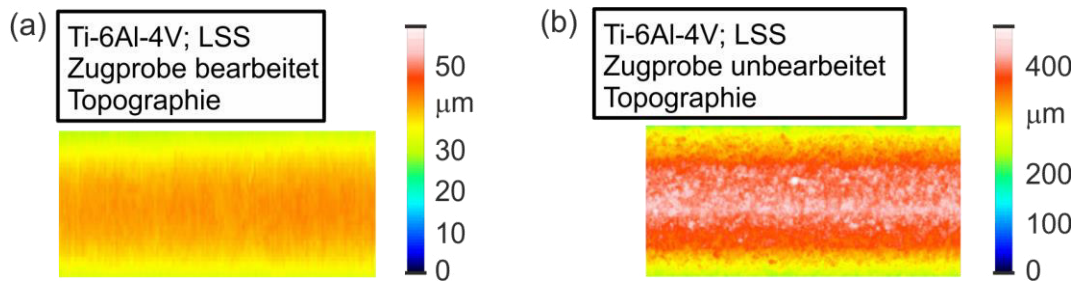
Topographie eines mittels Laserstrahlschmelzen gefertigten (a) bearbeiteten und (b) unbearbeiteten Zugprobe
